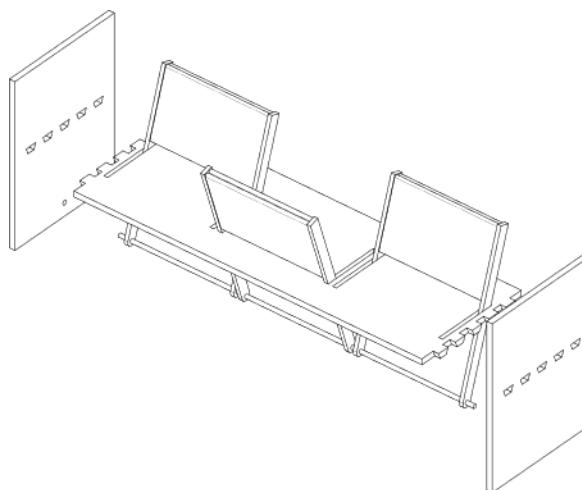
Esquema montaje conjunto 2 (elaboración propia, 2025)
